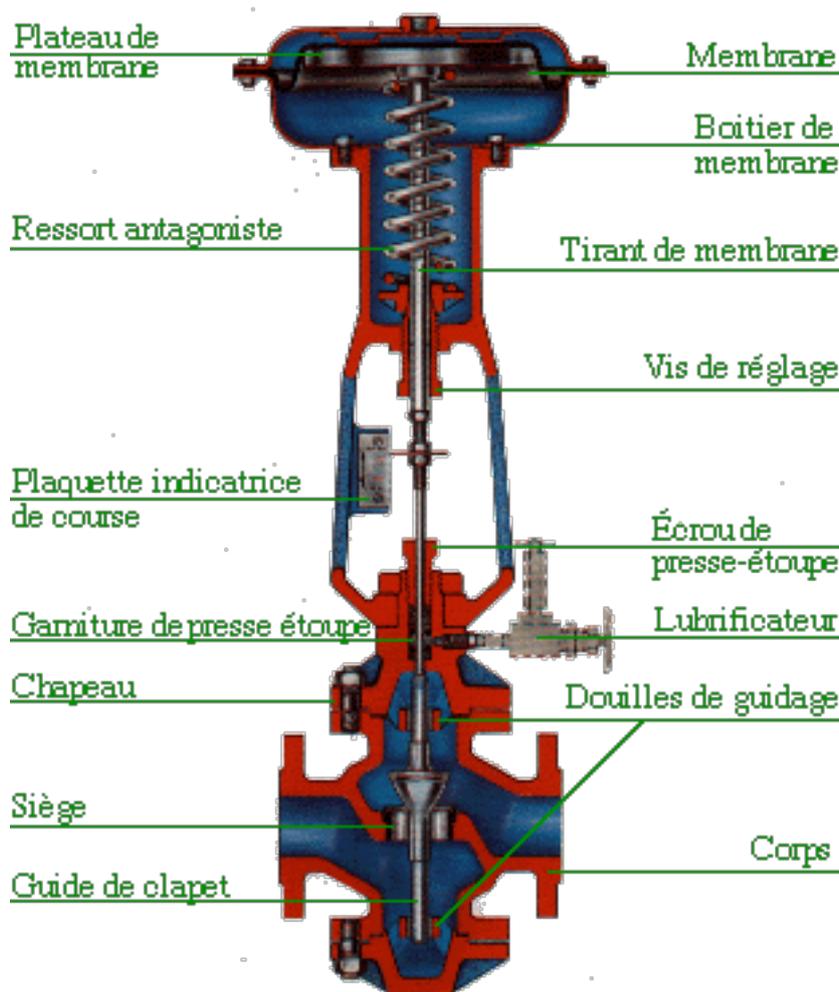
Vue en coupe d'une vanne de régulation pneumatique
